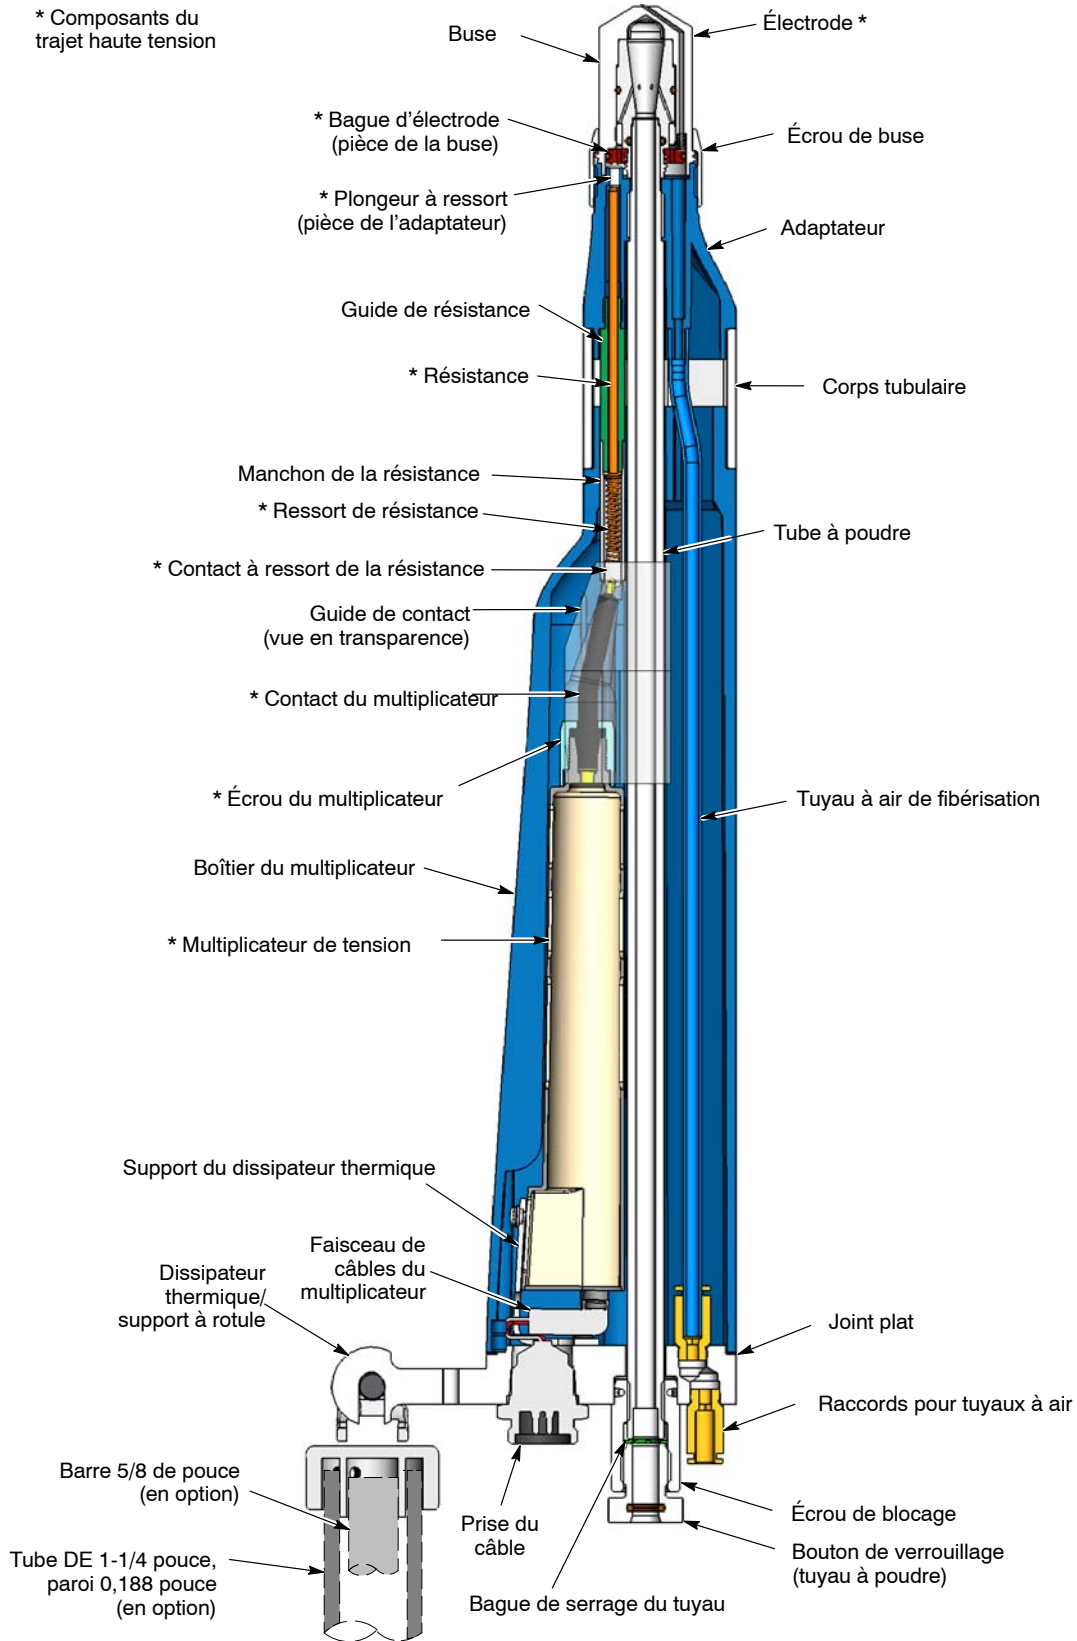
Vue en coupe – Composants et assemblage du pistolet à fixation sur barre
